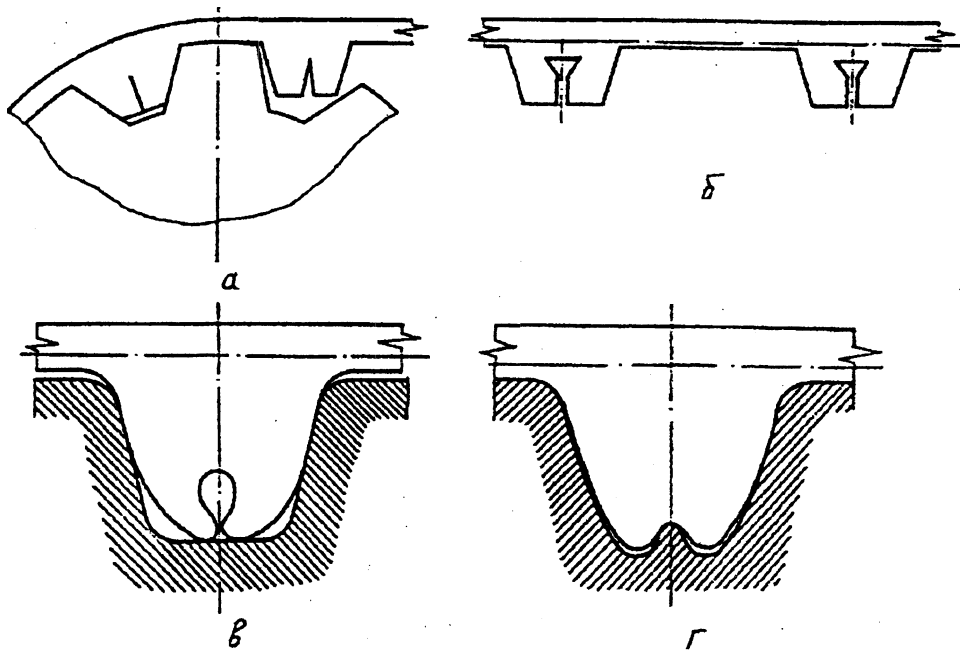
Конструкции зубчатых ремней с податливыми вершинами зубьев
